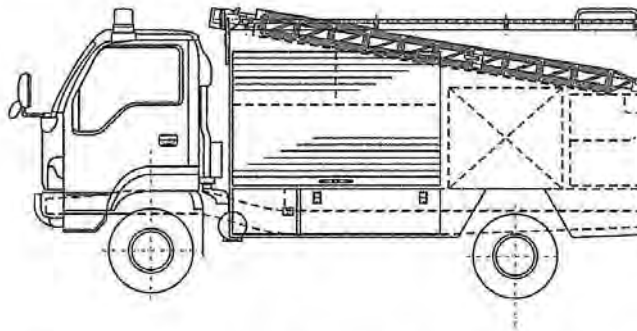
Plan de profil du fourgon pompe tonne 1.000 litres
